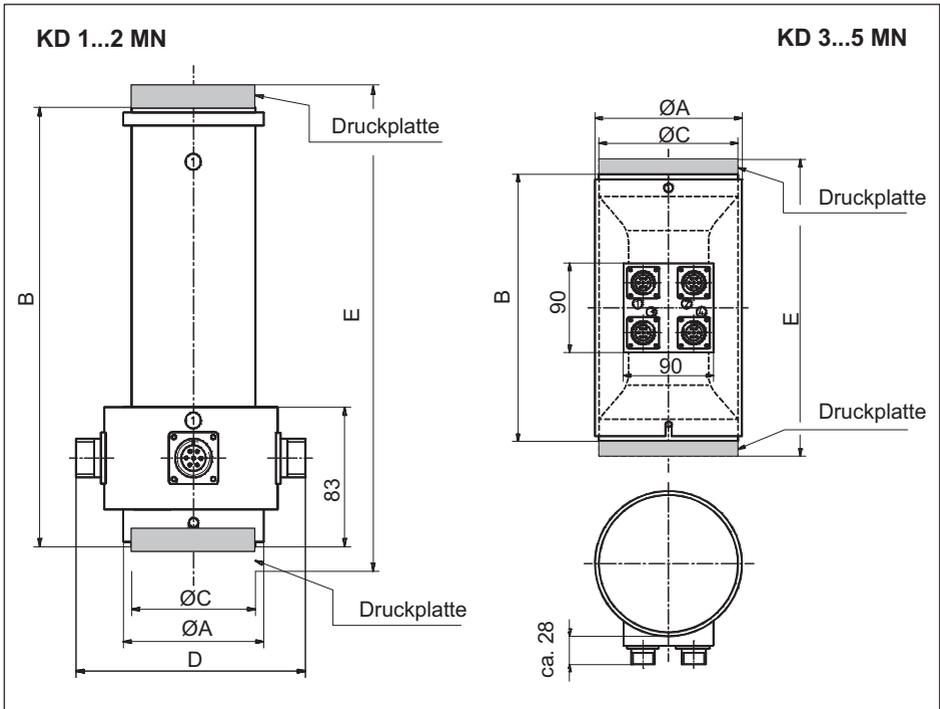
KD Kraftaufnehmer mit Druckplatten
